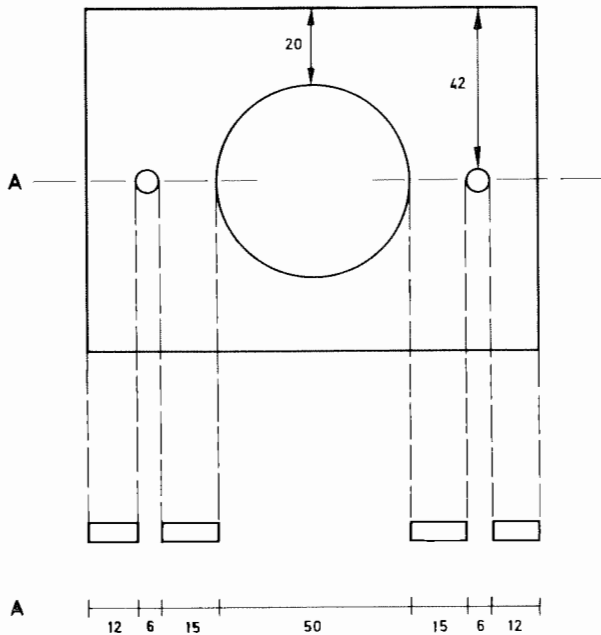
Duraluminiumplatte mit zentraler Bohrung und zwei peripheren Schraubenbohrungen; Grundelement des Folienprüfgerätes. (Bei „A“ Längsschnitt durch die Platte.) Alle Maßangaben in Millimetern.
